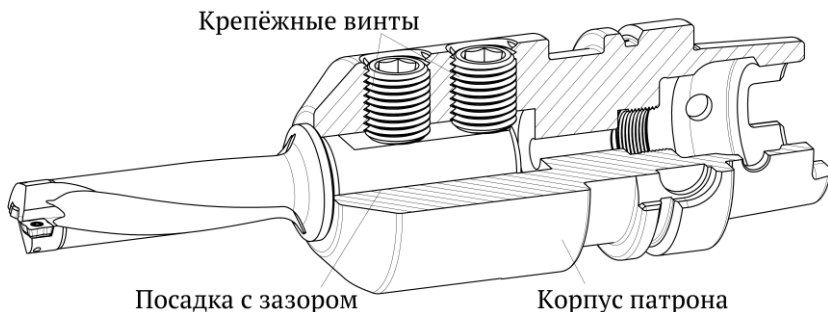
Патрон для хвостовика с лыской и сборное сверло
